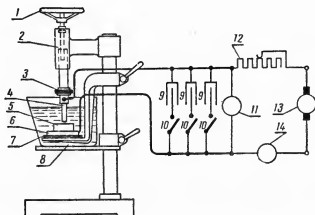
Станок для электронискрового изготовления полостей и отверстий в металле:
